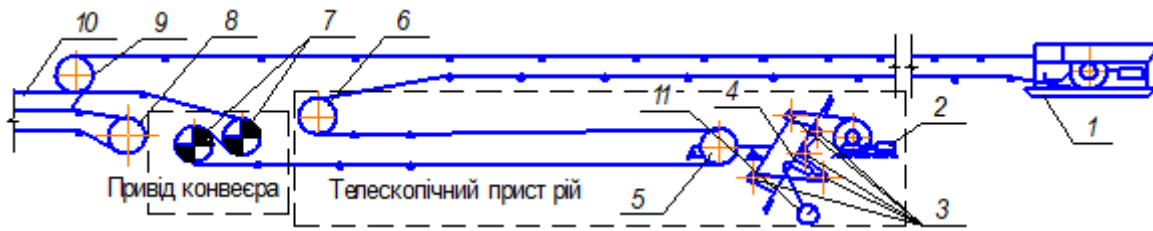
Схема стрічкового конвеєра зі змінною довжиною транспортування: 1 – пересувна станція; 2 – натяжна лебідка; 3 – обвідні блоки для канату; 4 – датчик натягнення канату; 5 – рухома каретка з барабаном; 6 – нерухомий барабан; 7 – приводні барабани конвеєра; 8 – кінцевий барабан наступного конвеєра; 9 – виносний барабан; 10 – тічка пересипу; 11 – пристрій, що перетворює силовий сигнал в аналоговий (електричний).
